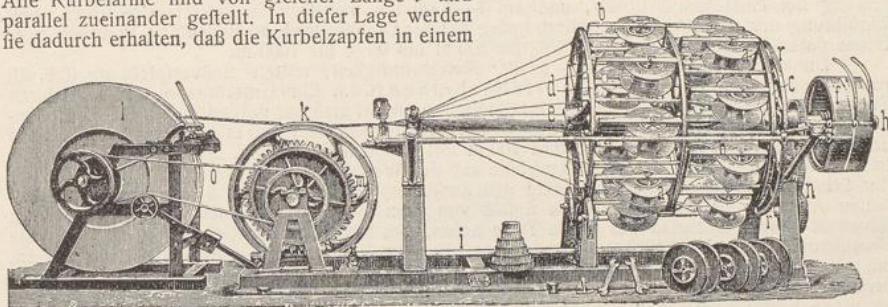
Seilschlagmaschine mit 18 Rollen.
